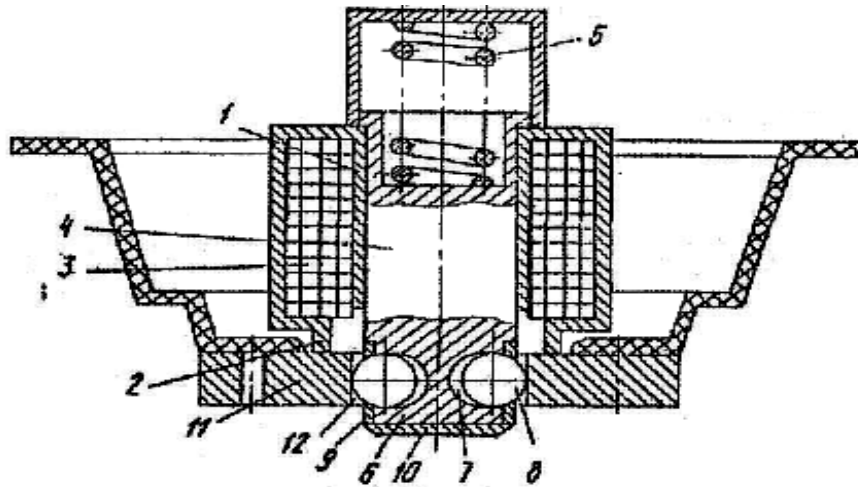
Електромагнітний захват в положенні захвату деталі
